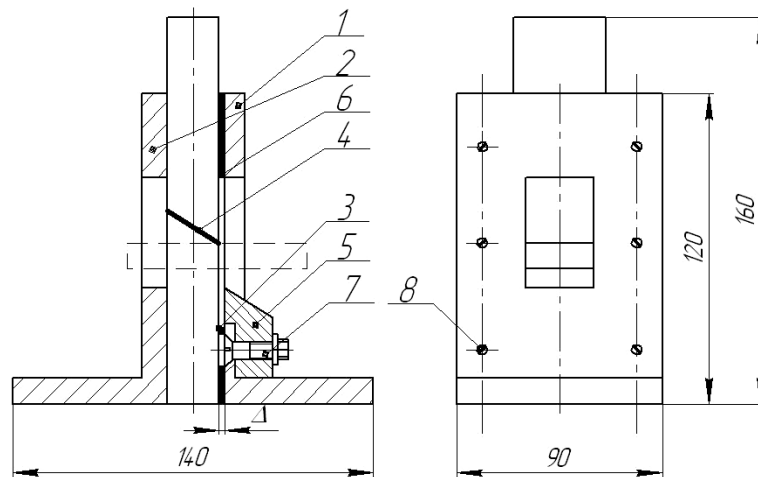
Пристрій для випробування зразків м'язової тканини ВРХ на зріз: 1,2 – стояки; 3 – вставка; 4 – ніж рухомий; 5 – ніж нерухомий; 6 – прокладка бронзова; 7,8 – різьбові з'єднання
